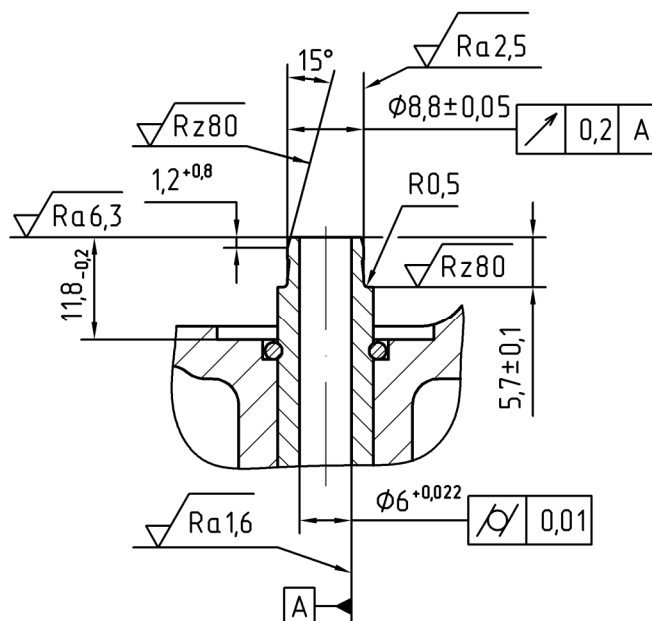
Обработка направляющих втулок клапанов после запрессовки их в головку цилиндров
